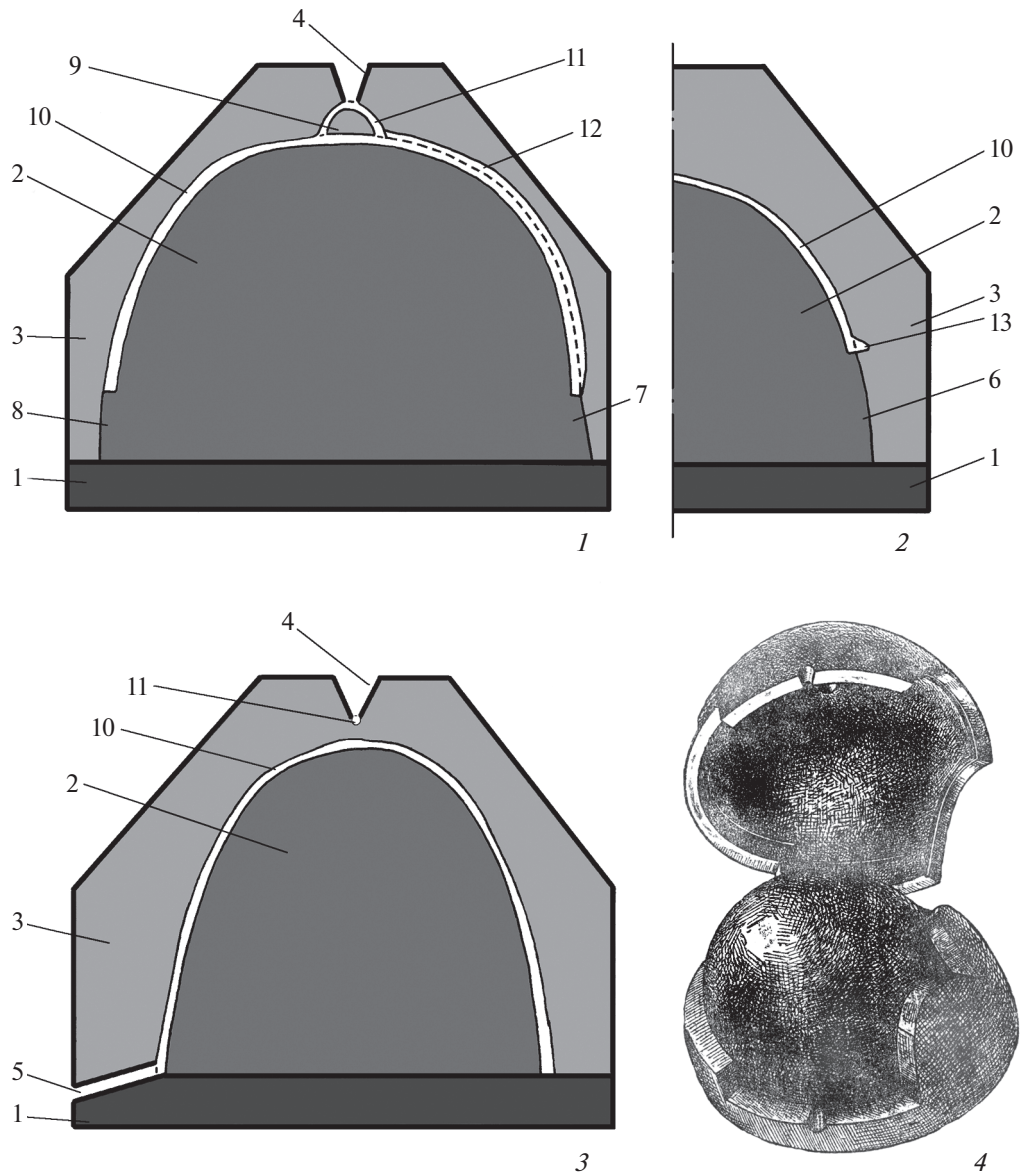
Реконструкция литейной формы для шлемов кубанского типа: 1 – центральный продольный разрез формы; 2 – часть бокового продольного разреза формы; 3 – поперечный разрез формы; 4 – вид двухчастной литейной формы для отливки шлема (по: Рабинович, 1941. Рис. 3). Составные части (1–3): 1 – подставка, 2 – стержень-болван (нижняя часть формы), 3 – верхняя часть формы, 4 – литник, 5 – выпор, 6 – выступ надглазничного выреза, 7 – выступ лицевого выреза, 8 – выступ шейного выреза, 9 – глиняная заформовка отверстия петли, 10 – модель стенки тульи, 11 – налипная модель наверхия-петли, 12 – налипная модель вертикального валика (реконструкция С.Б. Вальчака).
